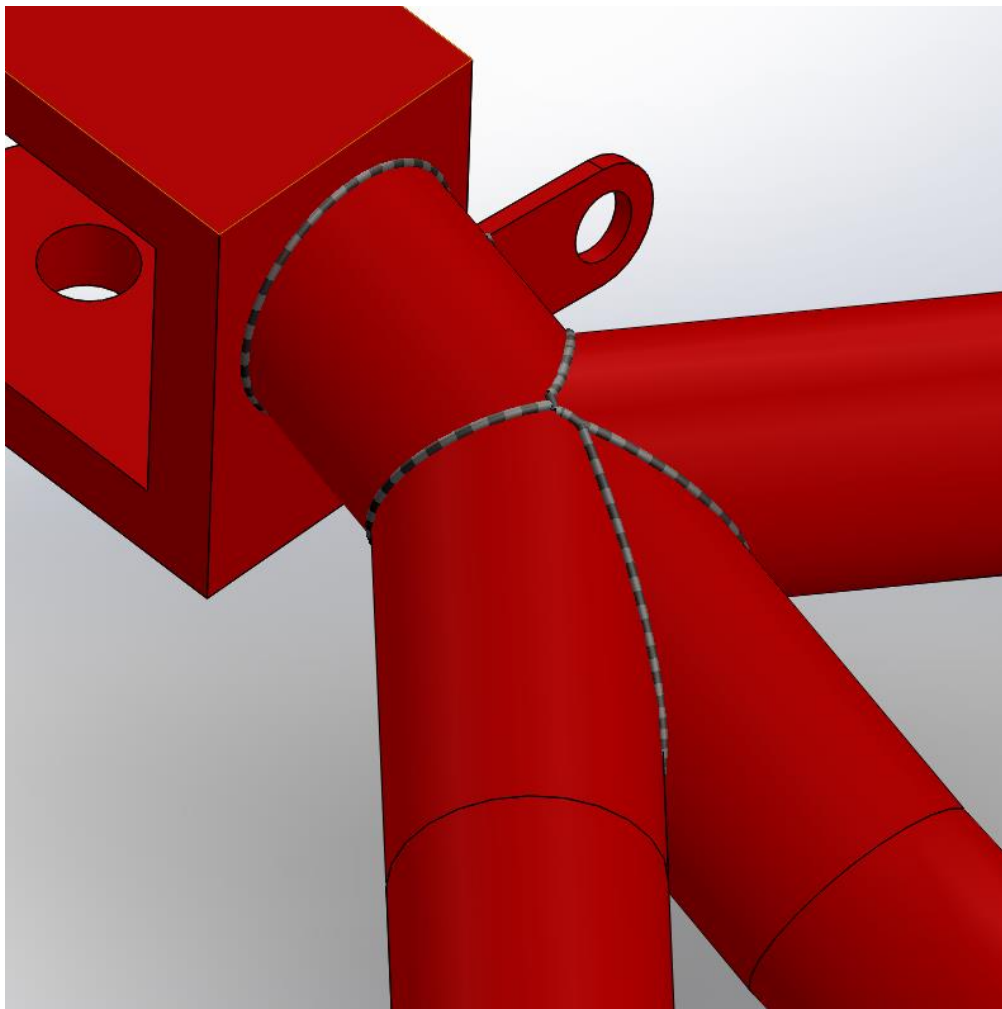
detalle cordones de soldadura. Fuente: propia.
